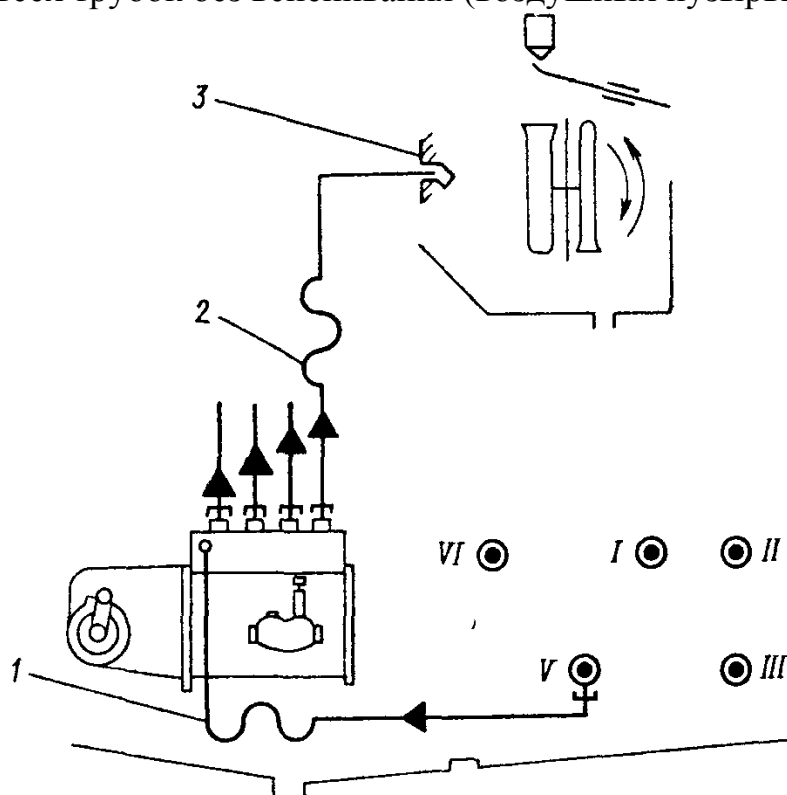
Схема соединения топливопроводов при испытании топливных насосов нагнетанием топлива в головку насоса под высоким давлением:
